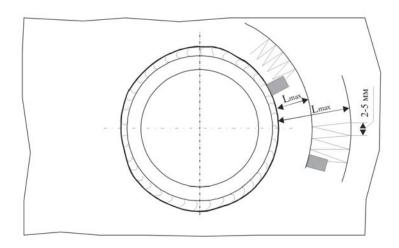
Схема сканирования углового сварного шва со стороны внутренней поверхности стенки PBC
